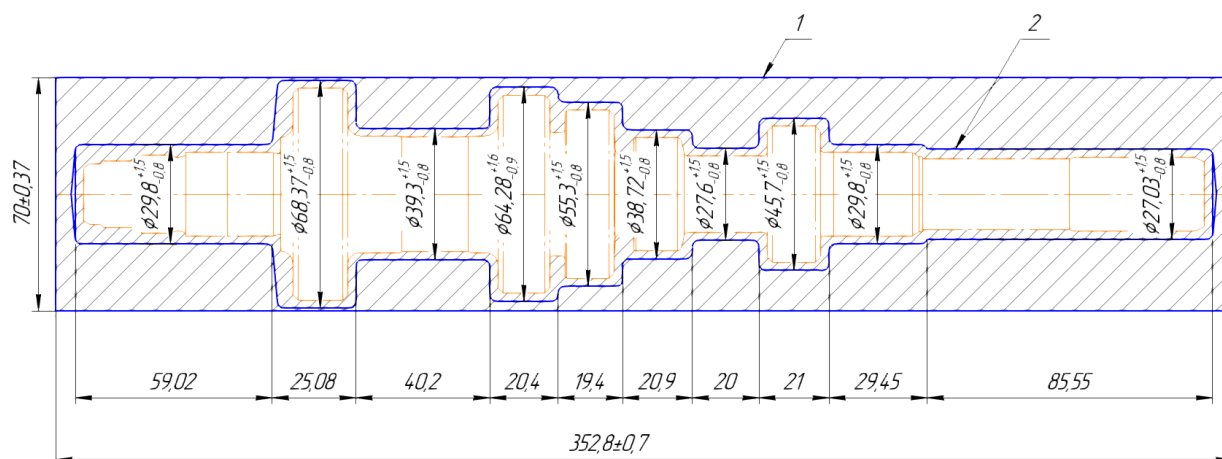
Контуры заготовок (1-прокат, 2- штамповка)
